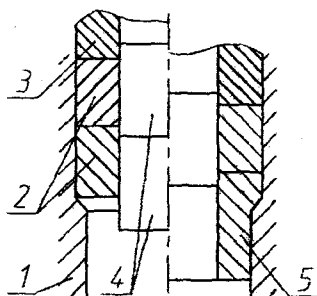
Штамповка трубных заготовок с активными силами контактного трения по внутренней поверхности: 1 – матрица для прямого выдавливания; 2 – заготовки; 3 – трубный пуансон; 4 – закаленные оправки; 5 – выдавливаемая деталь
